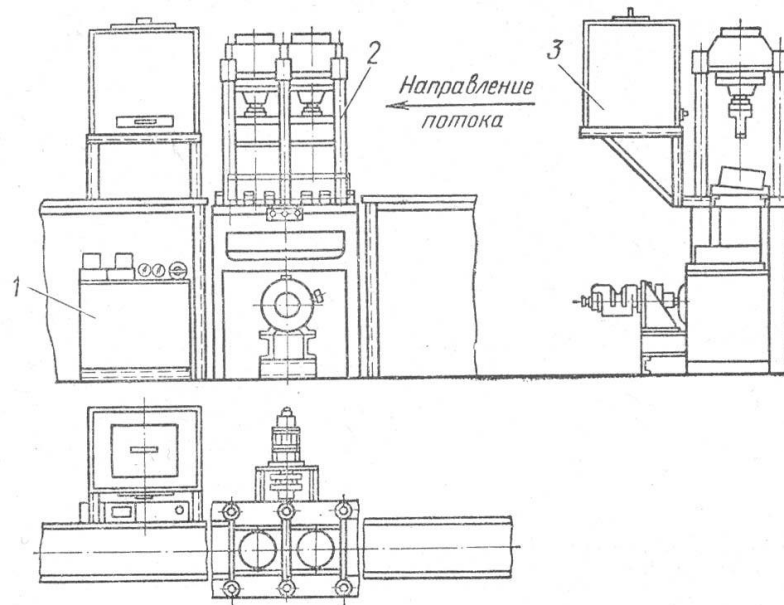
Установка для перепрессовки направляющих клапанів двигуна,
